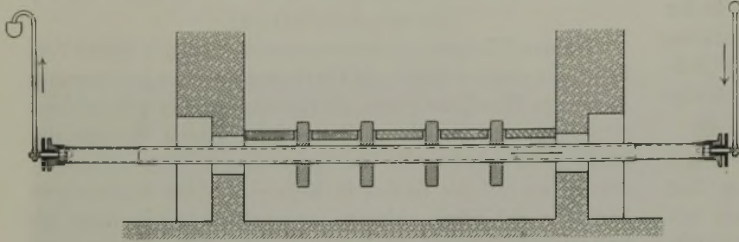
Tragscheiben auf wassergekühlter Hohlwelle mit Stopfbüchsen.
